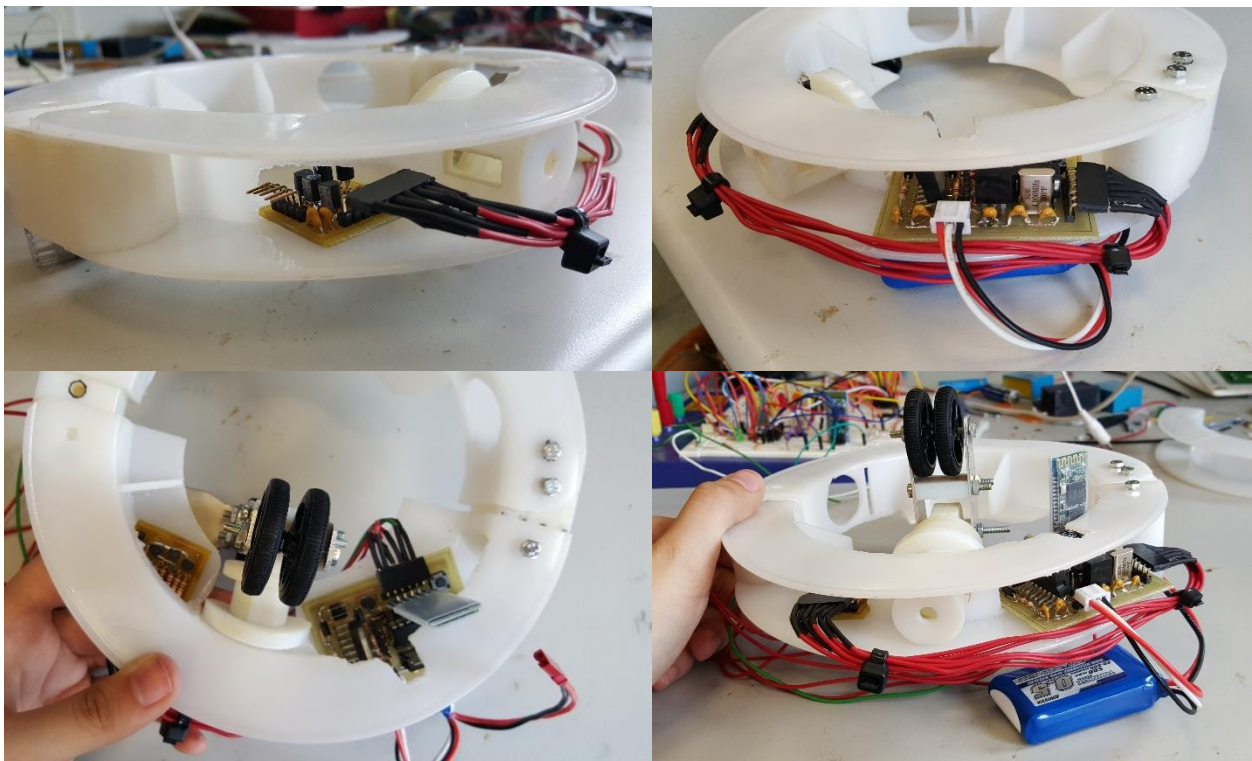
PCB principal y PCB de ampliación montadas
